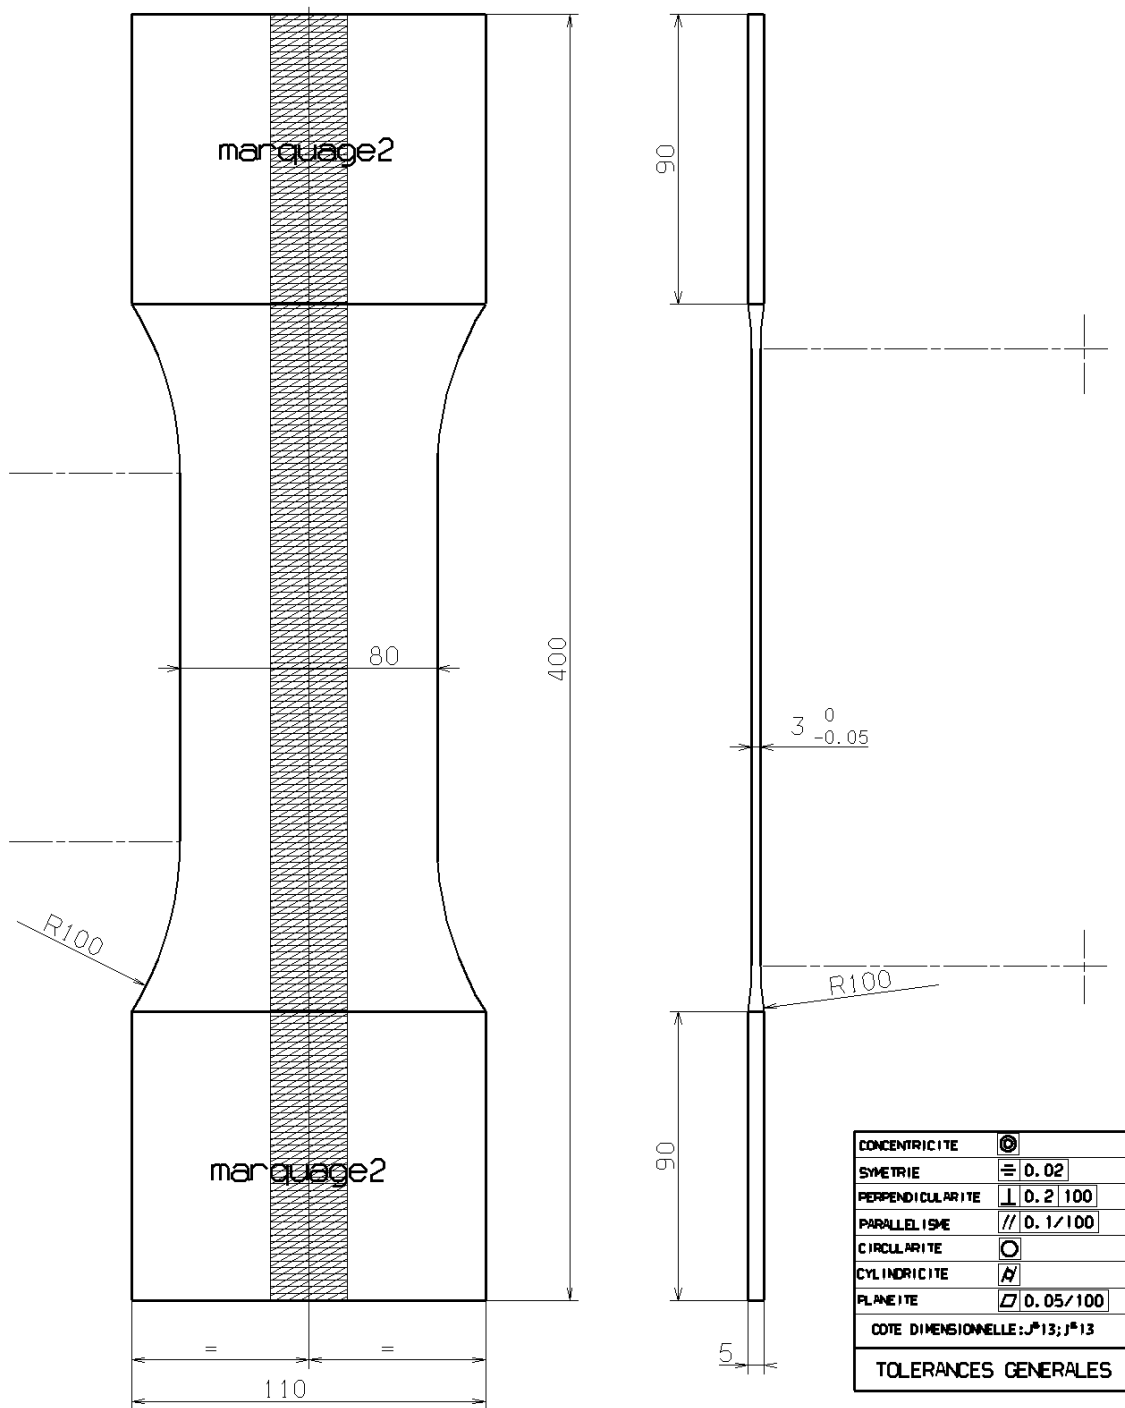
Géométrie d'éprouvette de traction monotone prélevées dans le sens L de plaques soudées par FSW(dites TPXXL)
